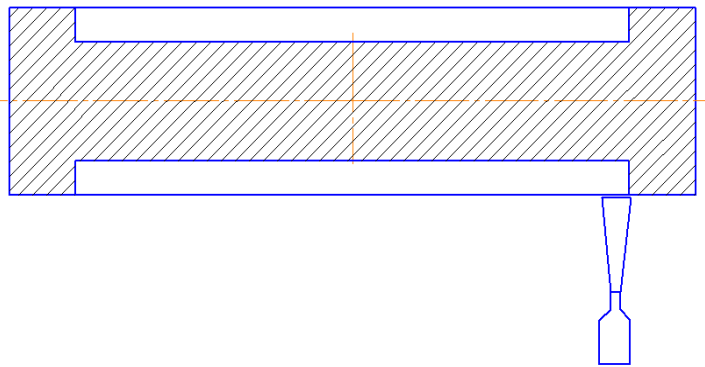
Чертеж детали «Колесо зубчатое»
